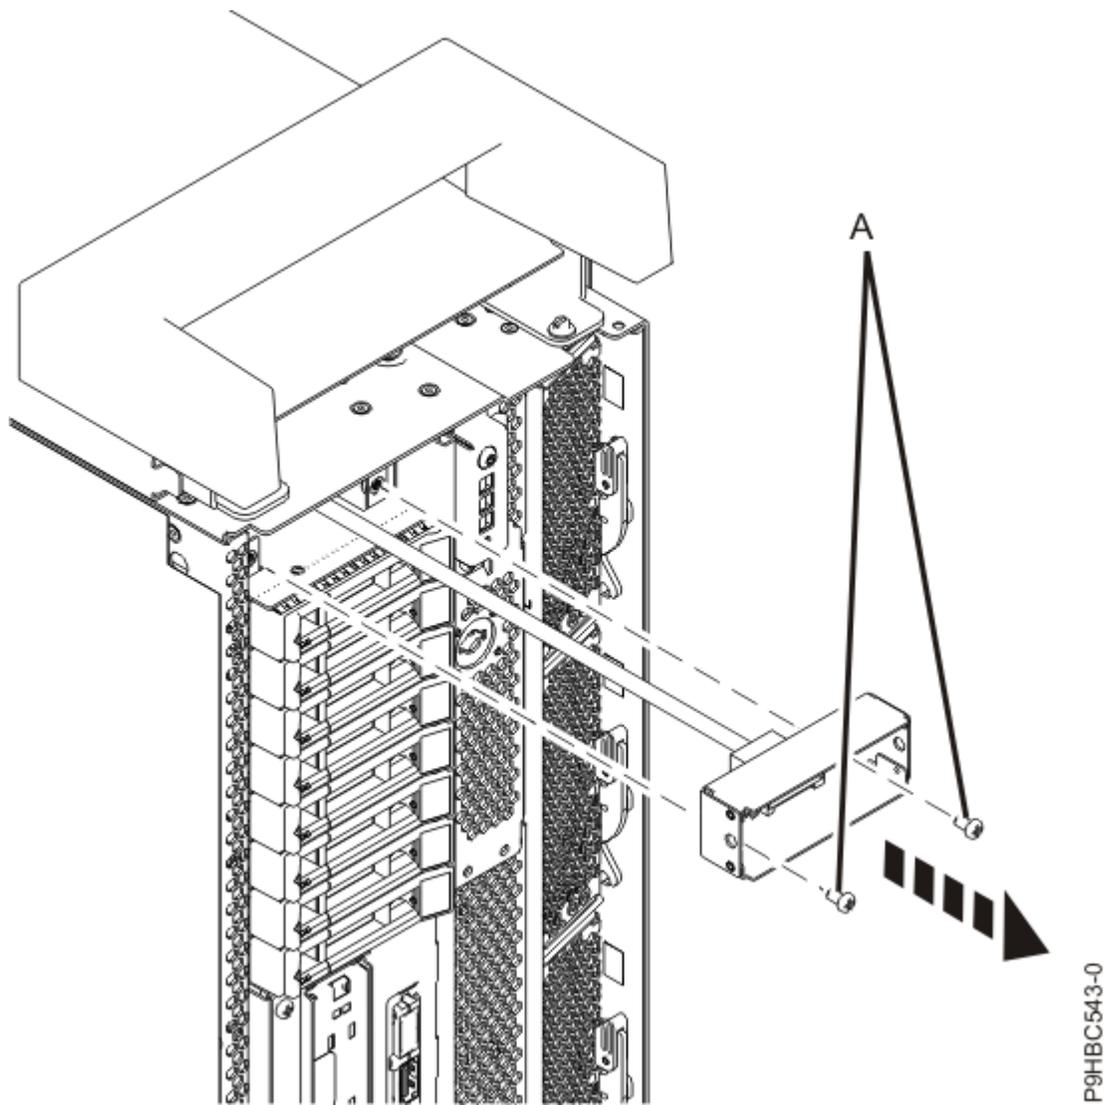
Remover o apoio do ecrã do painel de controlo do suporte para um sistema montado em bastidor
